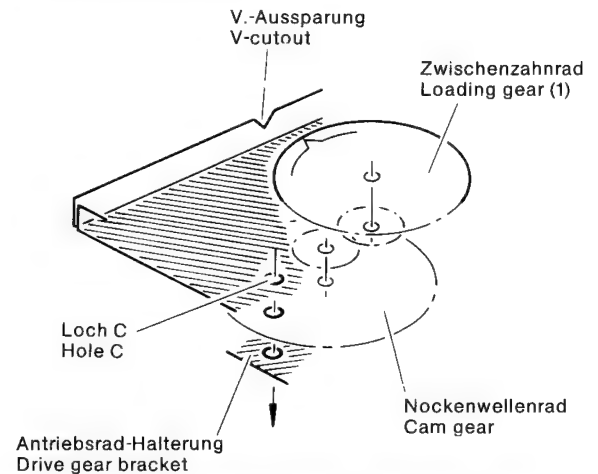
Nockenwellenrad/Zwischenzahnrad / Cam gear/loading gear (1)
